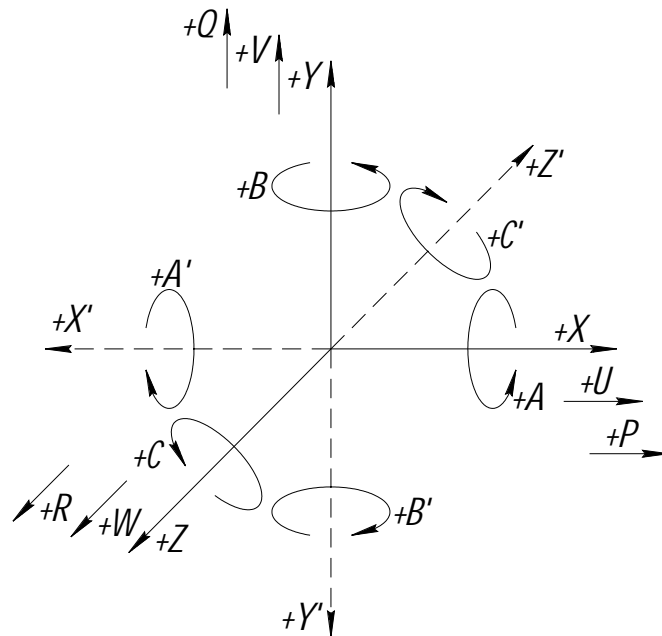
Стандартна система координат верстатів з ЧПК
